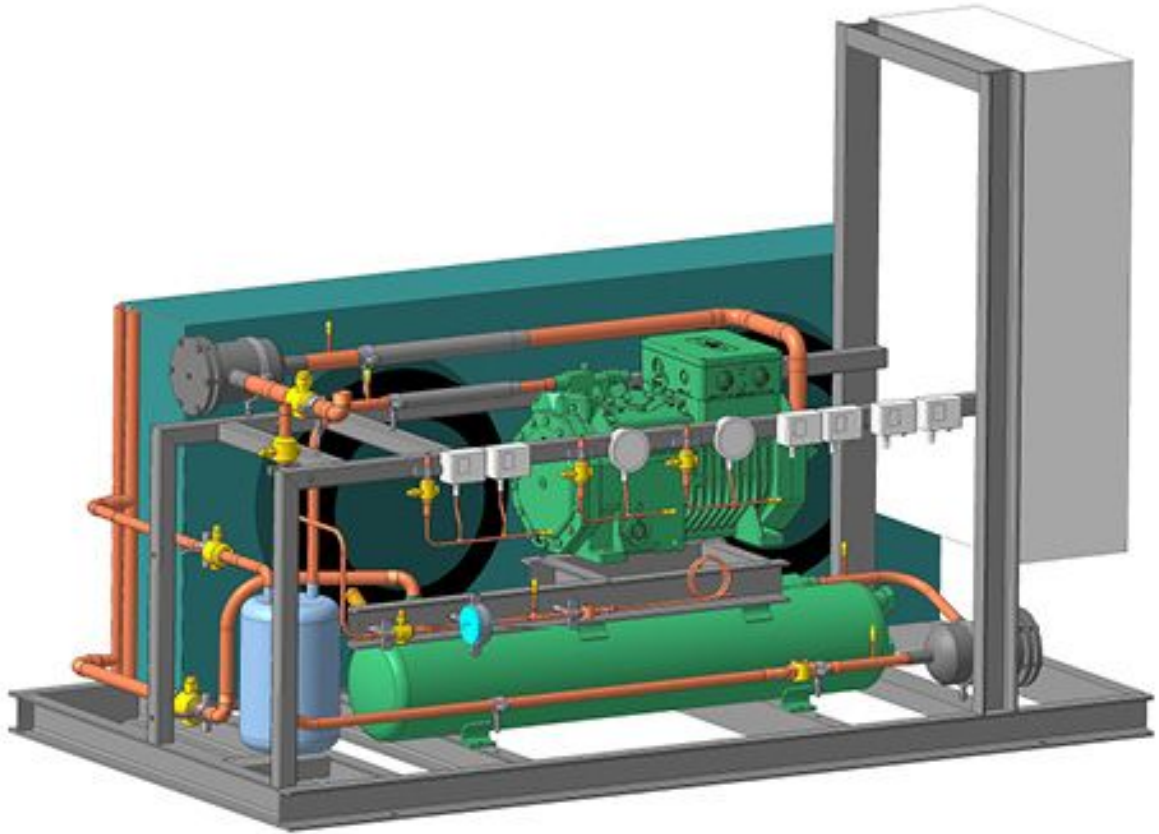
Компресорно-конденсаторний агрегат
